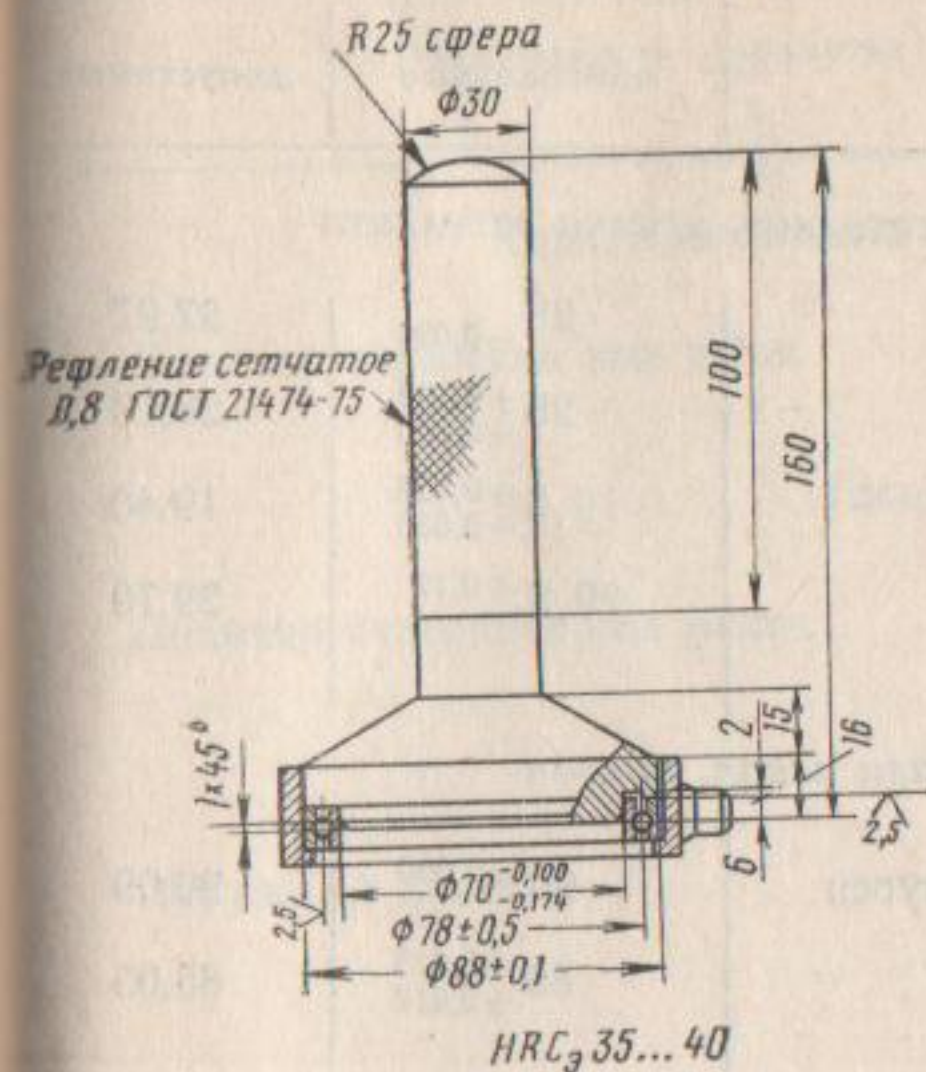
Оправка для установки подшипника в обойму механизма блокировки дифференциала заднего моста
